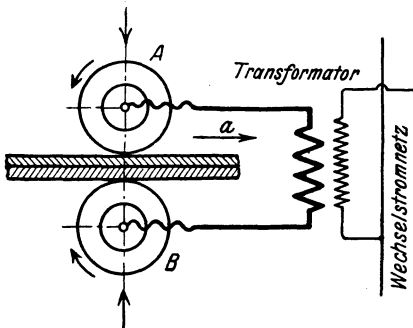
Schema der elektrischen Nahtschweißung.
